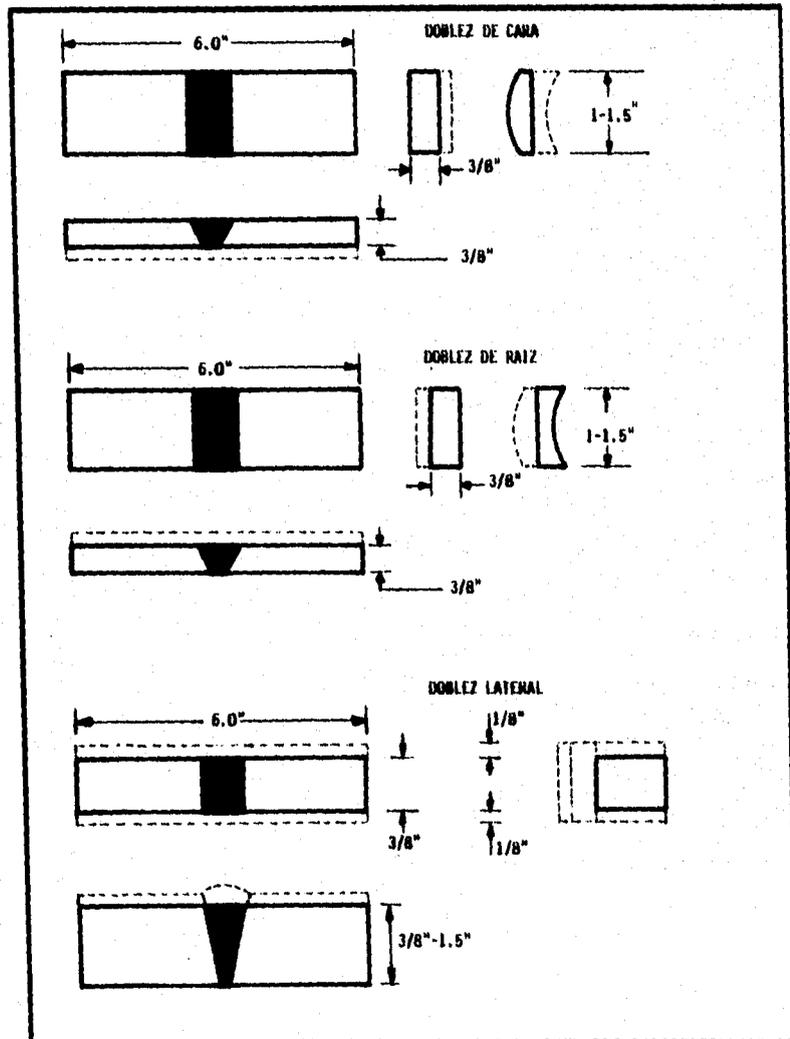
DIMENSIONES DE PROBETAS DE DOBLADO GUIADO.
